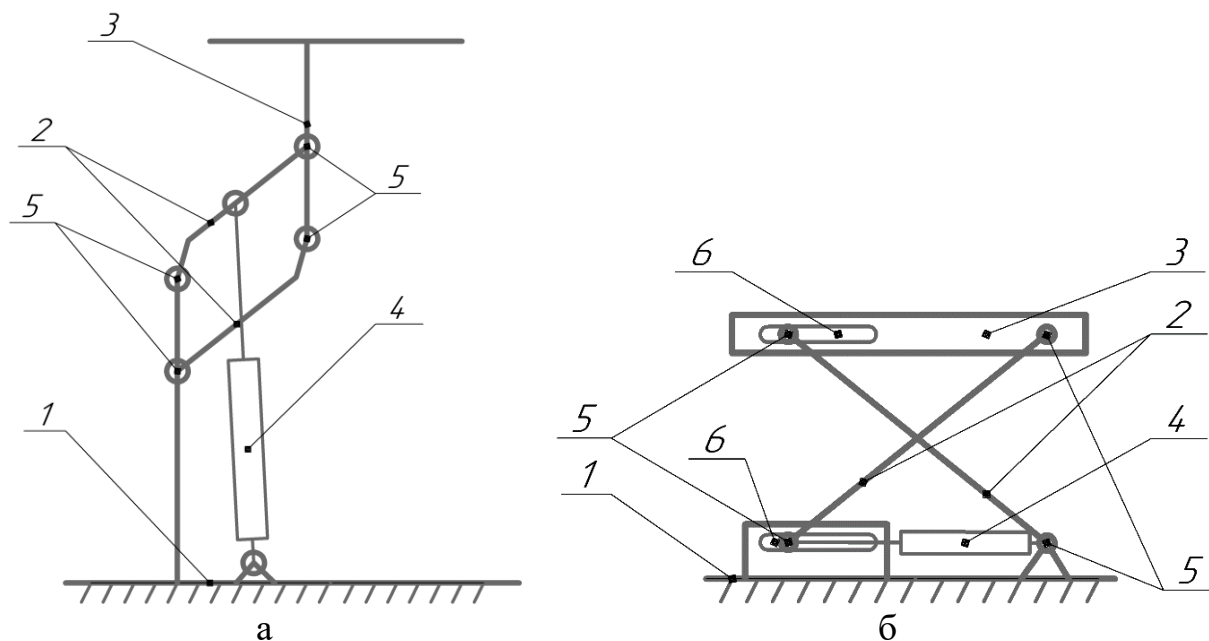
Варианты конструкций пространственных (рычажных, ножничных) механизмов: 1) нижняя стойка; 2) рычаги; 3) верхняя секция; 4) линейный привод*; 5) шарнир; 6) направляющая для подвижного шарнира
